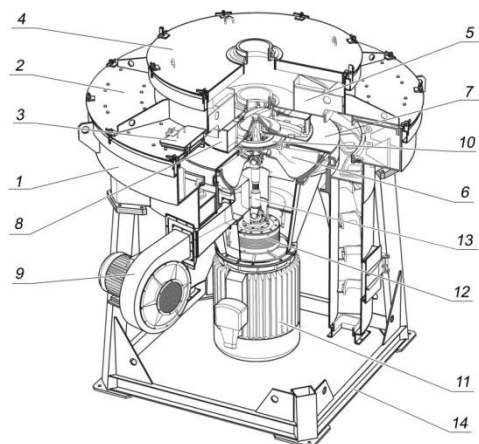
Устройство центробежной дробилки [1]: 1 – корпус с камерой измельчения выгрузными патрубками; 2 – крышка корпуса; 3 – смотровой люк; 4 – крышка (с загрузочной воронкой); 5 – внутренняя вставка с воронкой; 6 – воздушно-опорный узел; 7 – крышка воздушно-опорного узла; 8 – ускоритель; 9 – вентилятор наддува; 10 – подшипниковая опора; 11 – электродвигатель привода дробилки; 12 – муфта; 13 – карданный вал; 14 – рама
